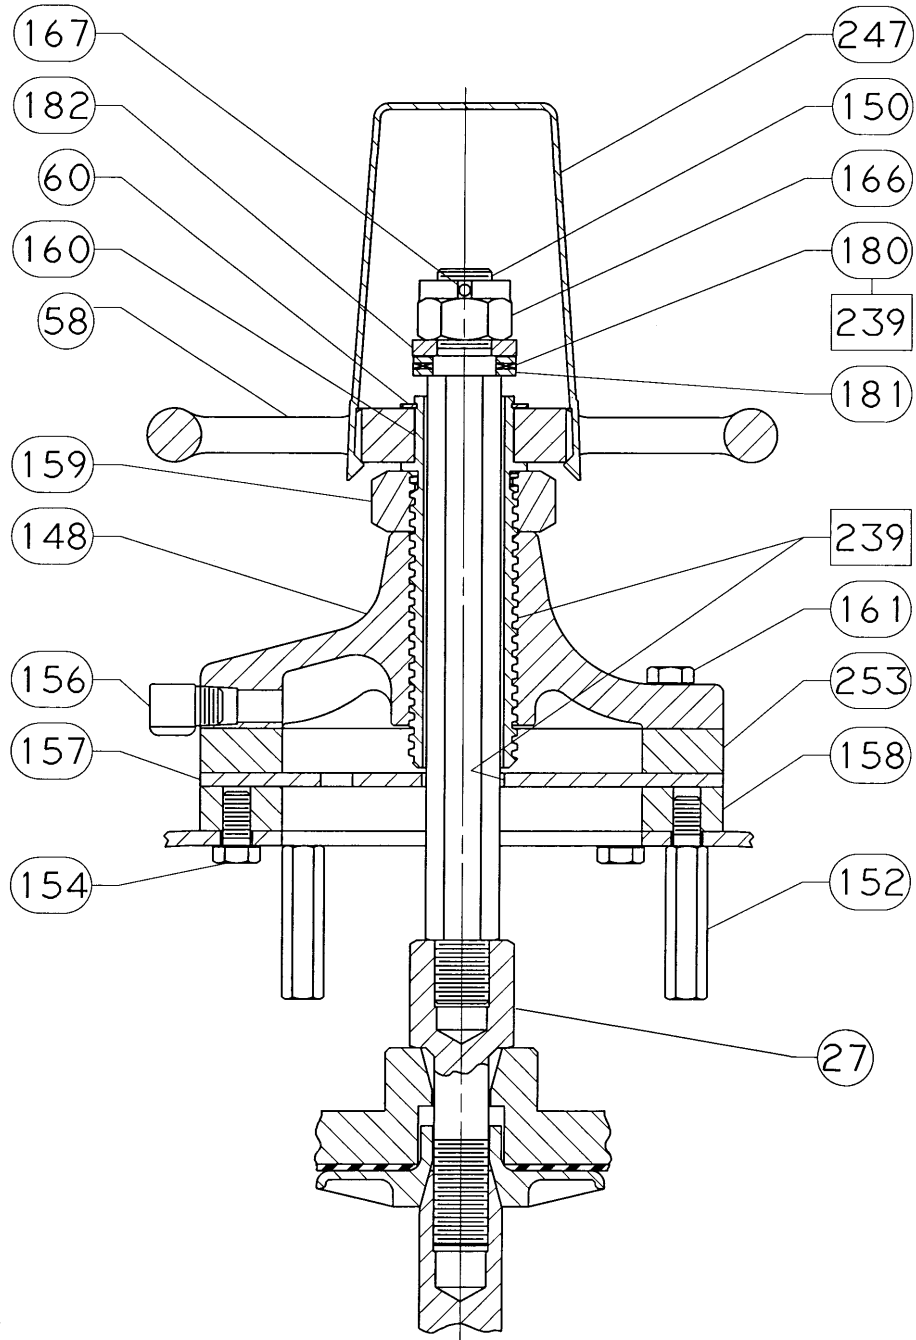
Верхний ручной дублер, тип P2 для приводов размером 45/45i, 50/50i, 60/60i и 76/76i
